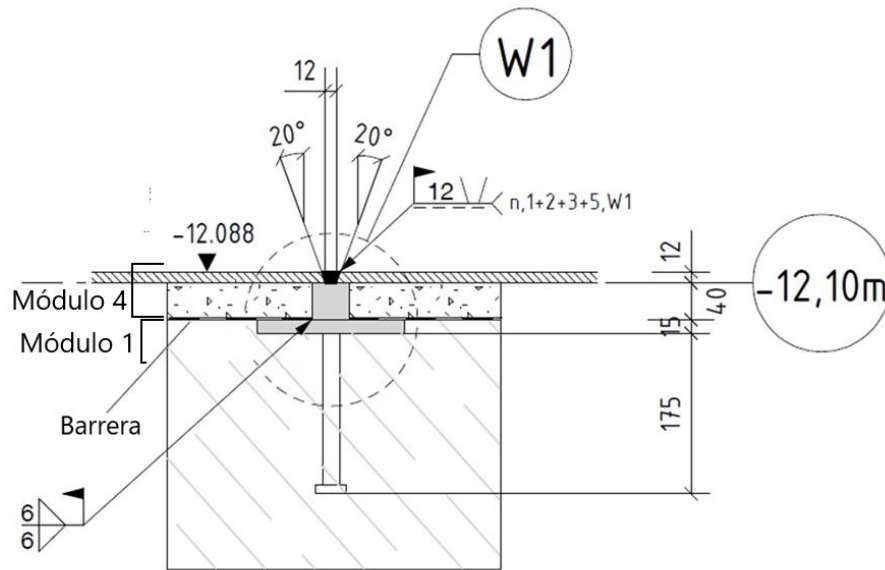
Plano en corte del Módulo 1 y 4. Fuente: Imagen extraída de los Welding Map elaborados por CONUAR.
